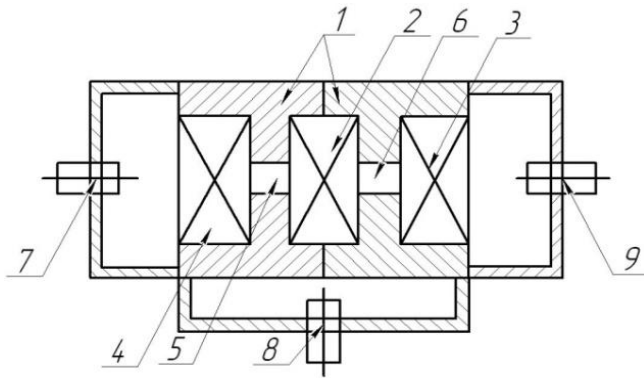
Схема ультразвукового датчика: 1 – корпус; 2 – излучатель; 3 – приемник; 4-дополнительный приемник; 5 – реперный канал; 6-измерительный канал; 7-9 – электроразъемы.
